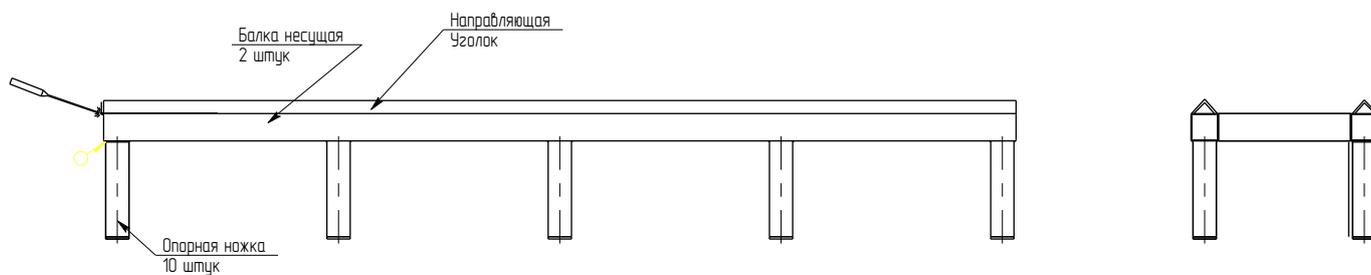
Соединение направляющего уголка со столом с помощью сварки
